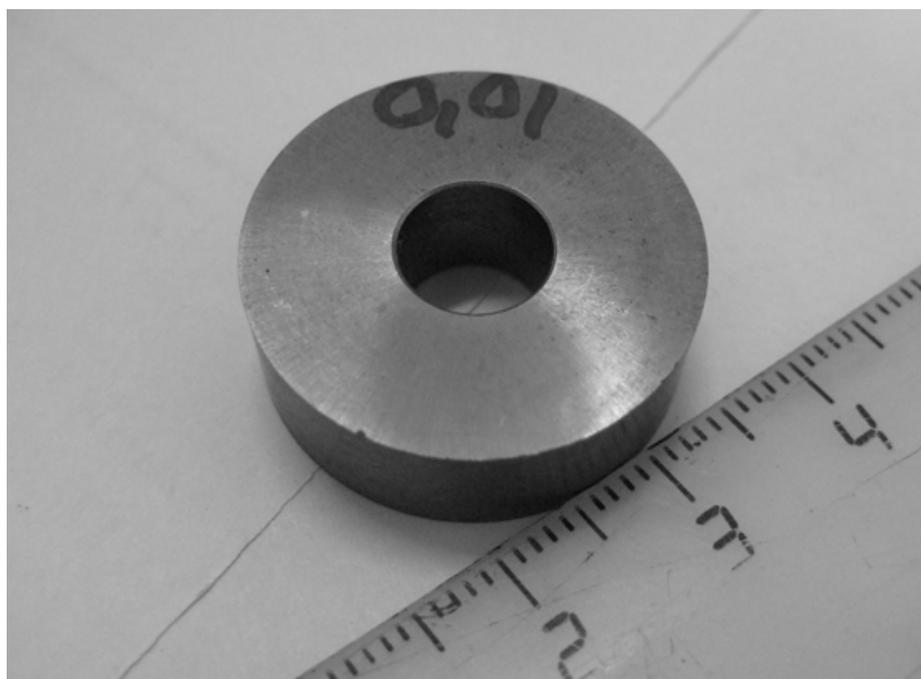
Вырезанная заготовка из спеченного твердого сплава под мелко модульную червячную фрезу на электроэрозионном станке.
